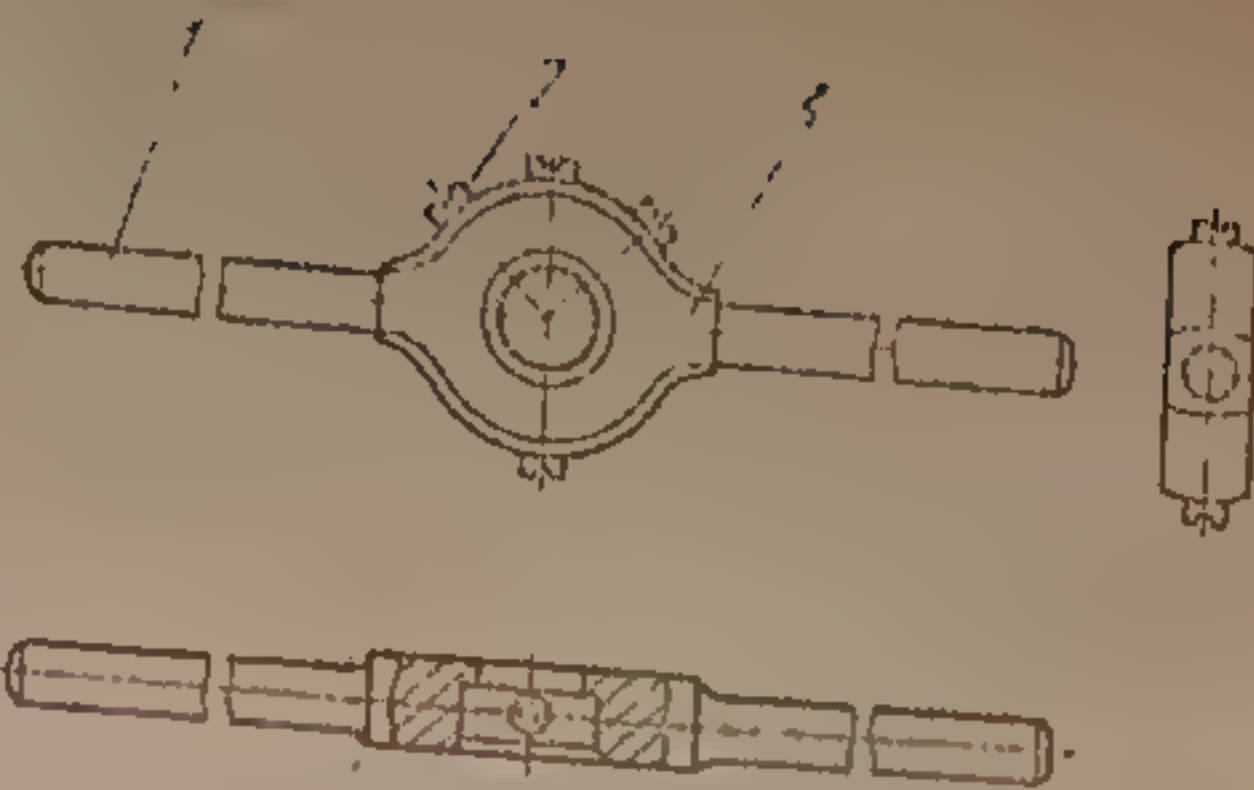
Вороток одногнездный: 1 — рукоятка; 2 — винт; 3 — корпус
